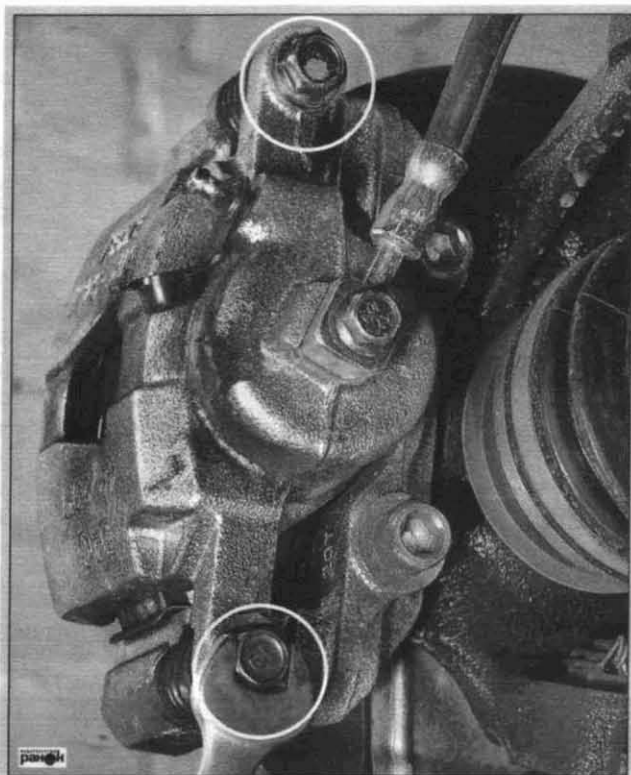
Суппорт тормозного механизма переднего колеса (выделены болты крепления скобы суппорта)
